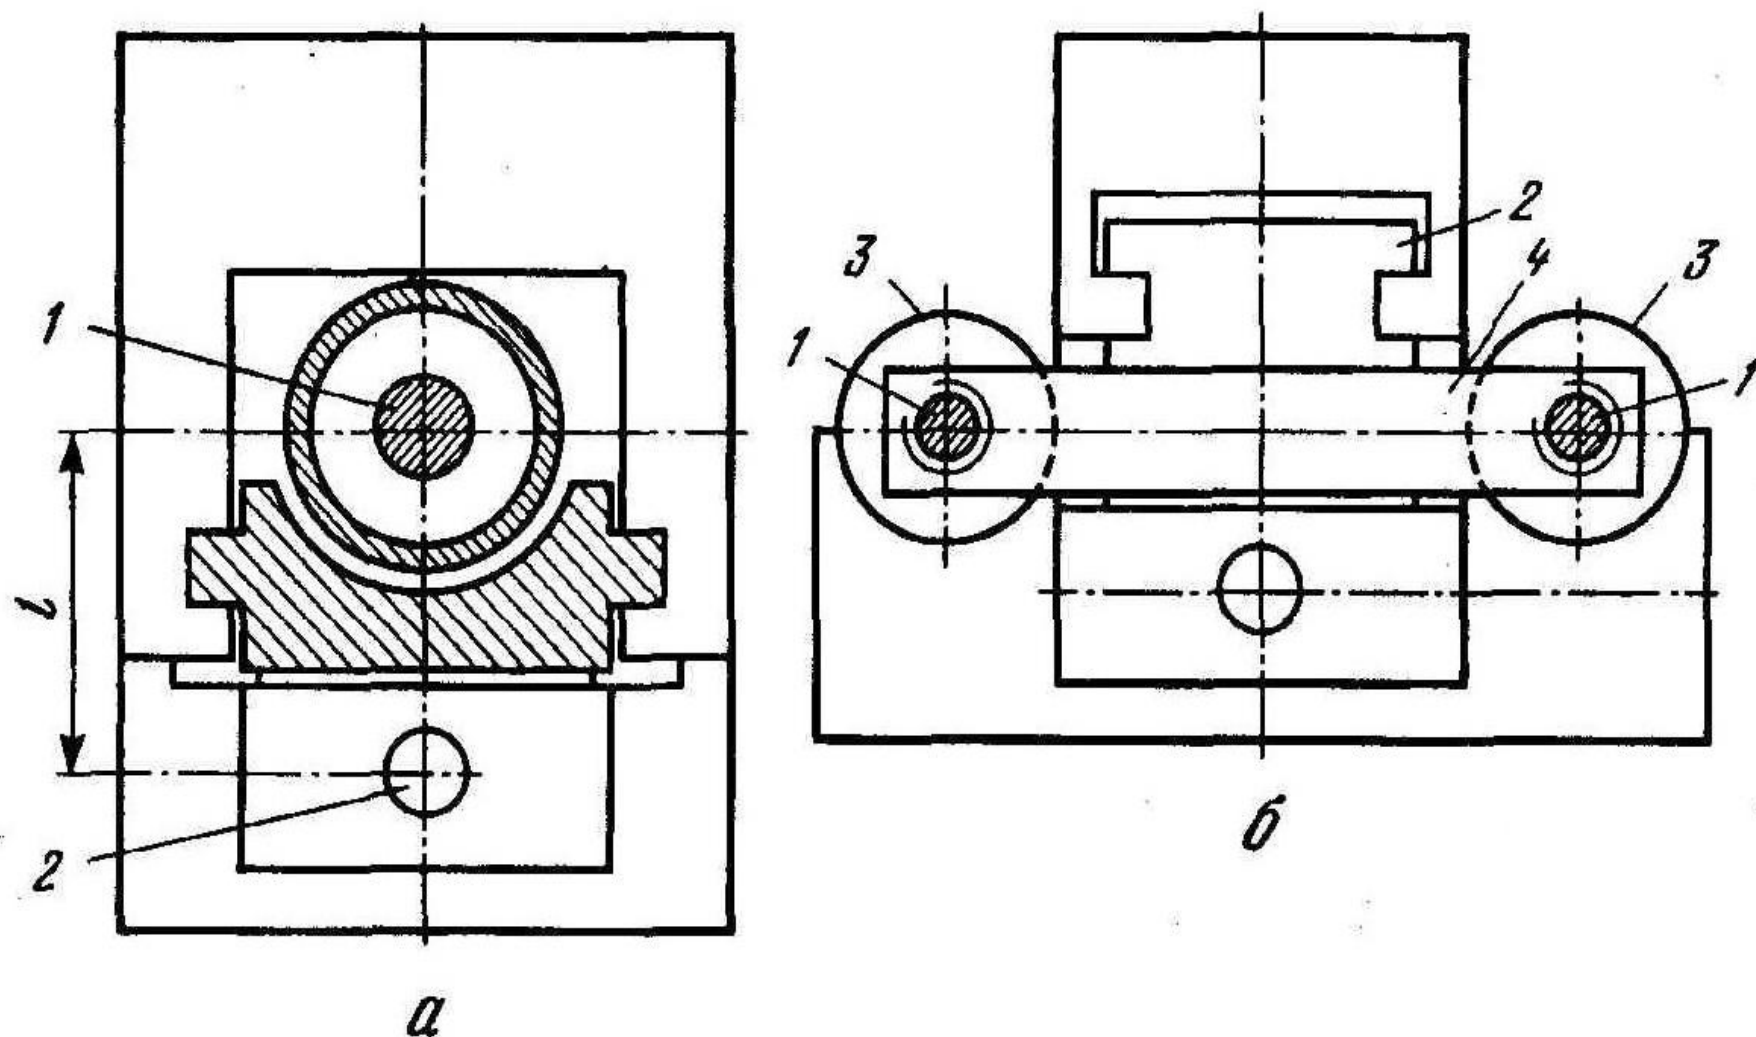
Схемы компоновки вертикально-протяжных станков с одним (а) и двумя (б) тянущими гидроцилиндрами.
